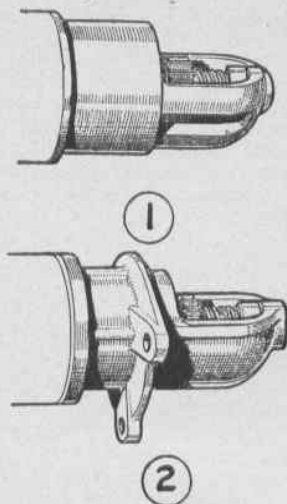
MONTAGE DU DEMARREUR SUR LE MOTEUR.
